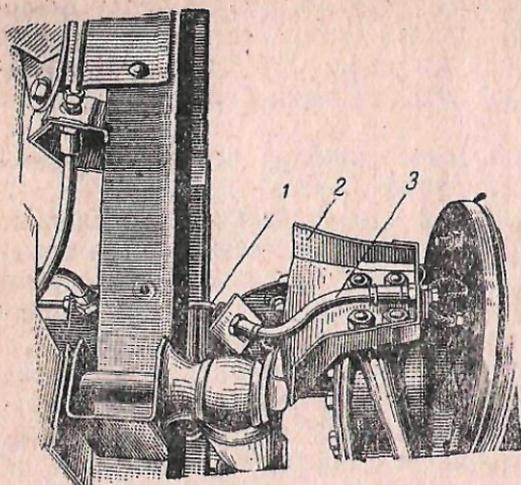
Защитное приспособление гибких шлангов привода тормозов передних колес:
